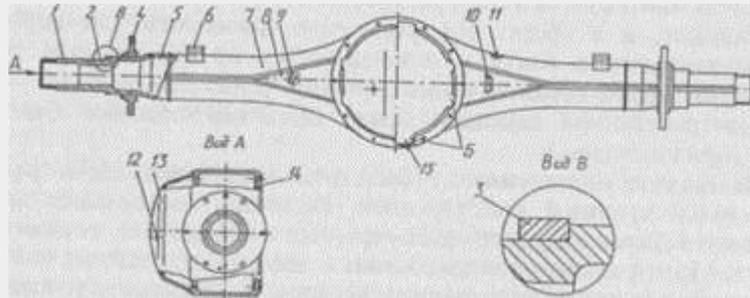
Конструкция штампованно-сварной балки типа «банджо»
